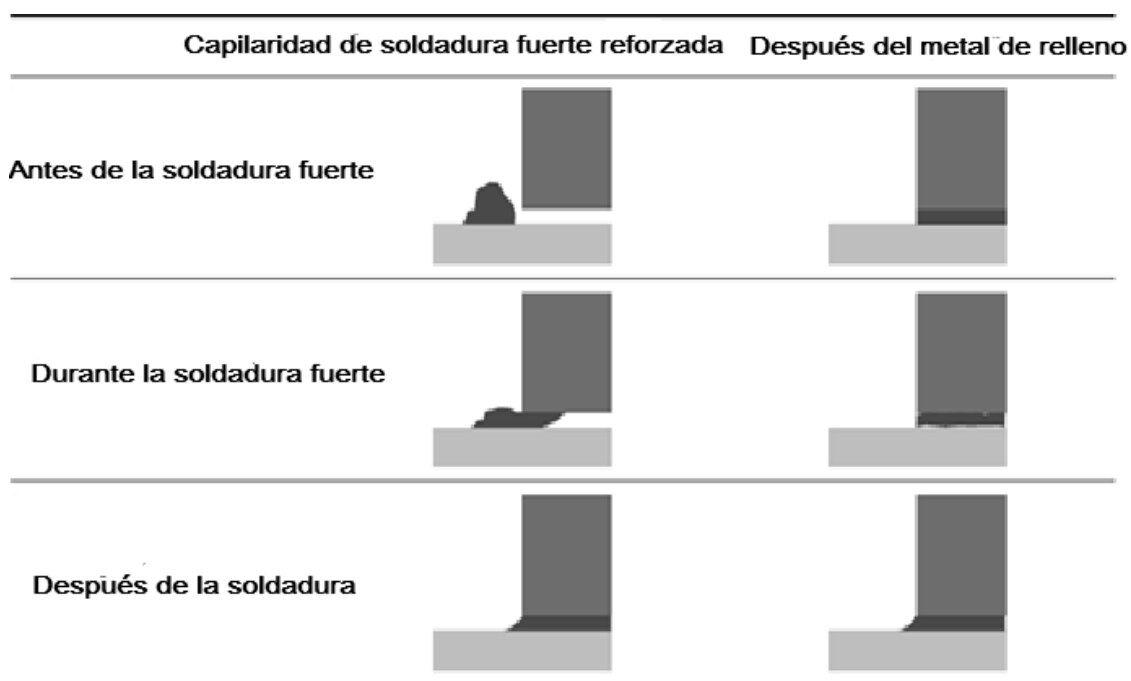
53 Capilaridad de las uniones soldadas [11].
